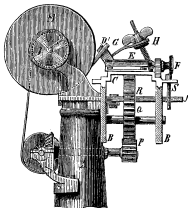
Vorrichtung zum Schleifen von Maschinenmessern. Querschnitt.
